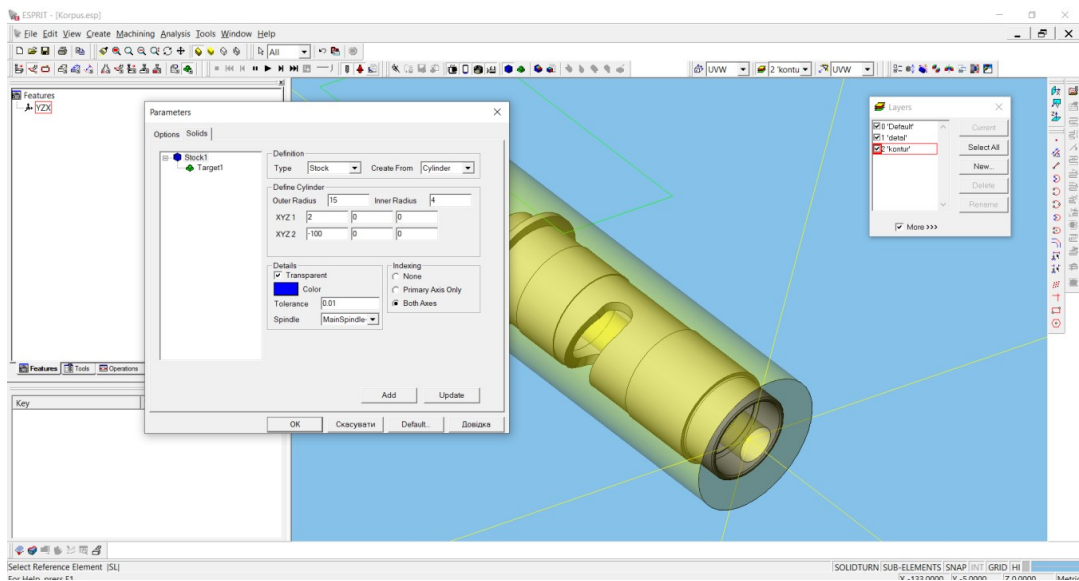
Прив'язка заготовки до головного шпинделя
